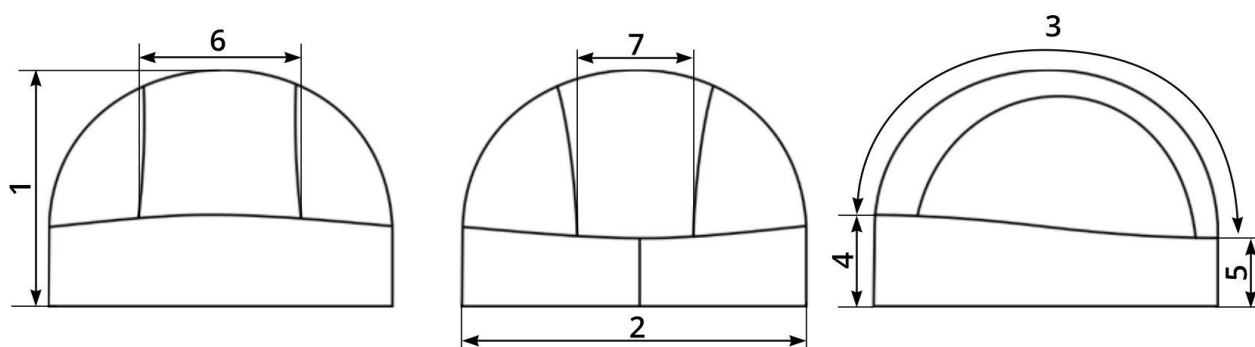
Зовнішній вигляд деталей предмета
